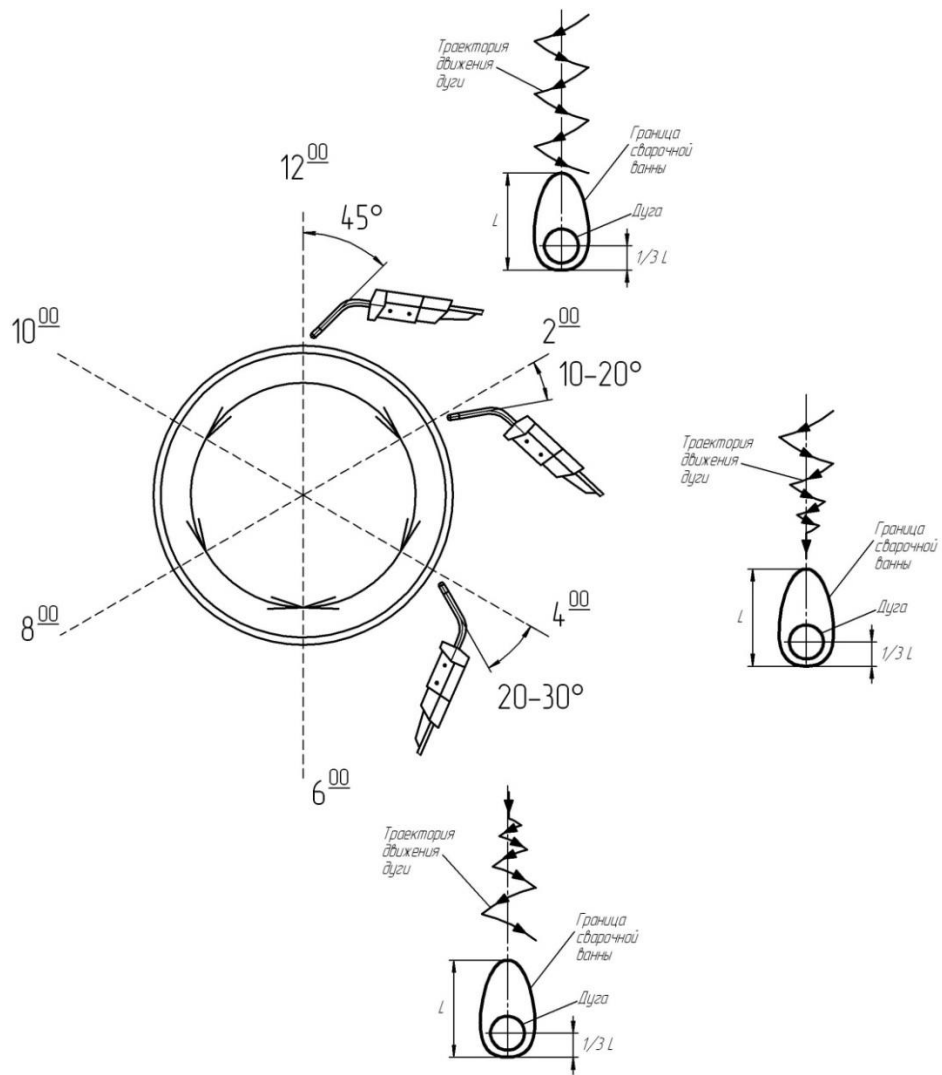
Техника сварки стыка труб по технологии STT
